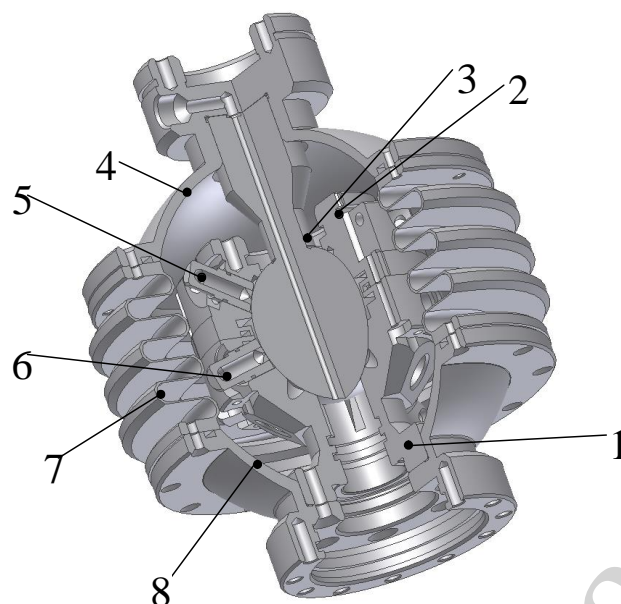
Конструктивне виконання регульованого сферичного гідростатичного опорного вузла: 1 – корпус; 2 – кришка; 3 – сфера; 4 – кожух верхній; 5, 6 – штуцери; 7 – сильфон; 8 – кожух нижній
